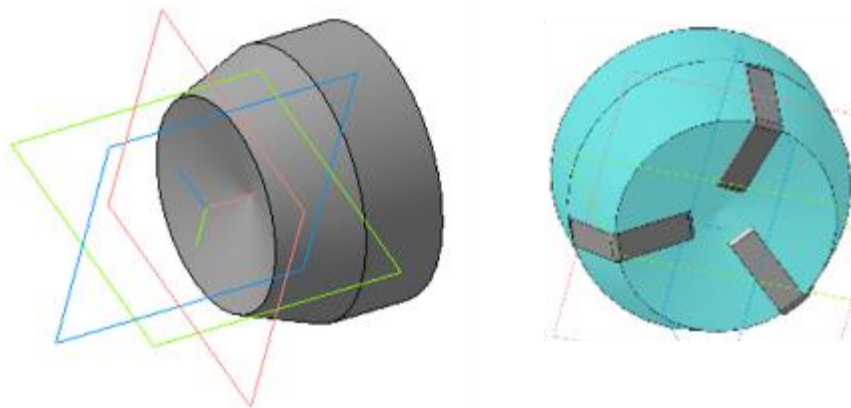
Розміщення БНП у корпусі різальних пластин
